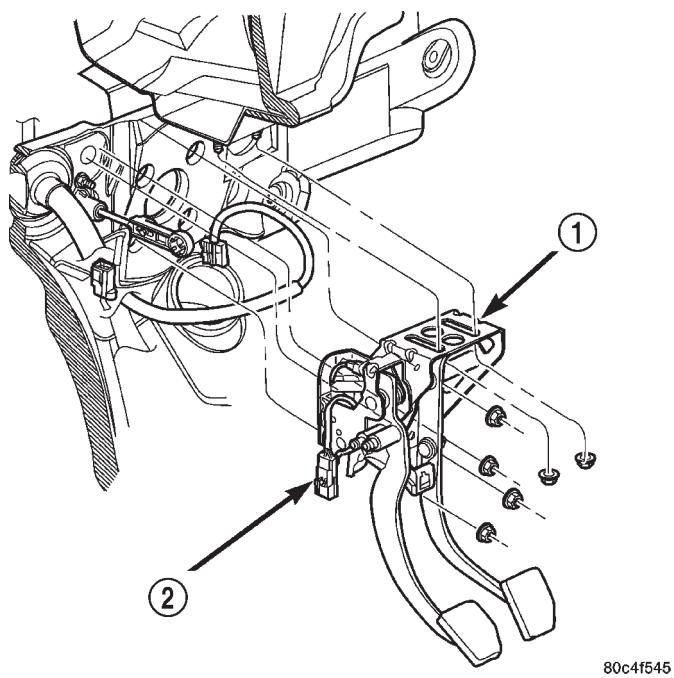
Desmontaje e instalación del conjunto de pedal de freno y embrague
